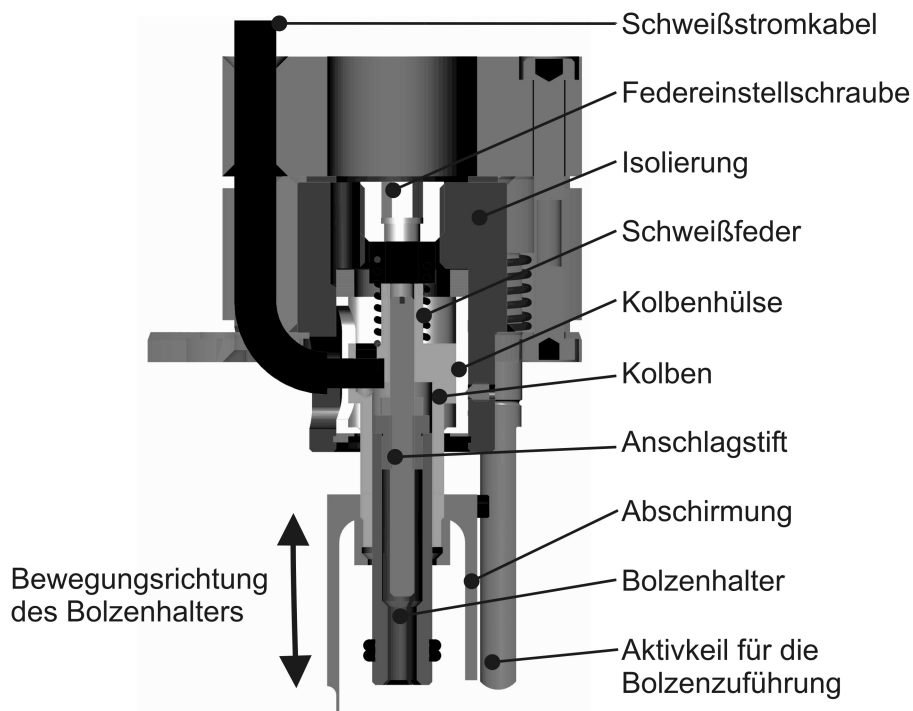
Schnittbild des Schweißkopfes
